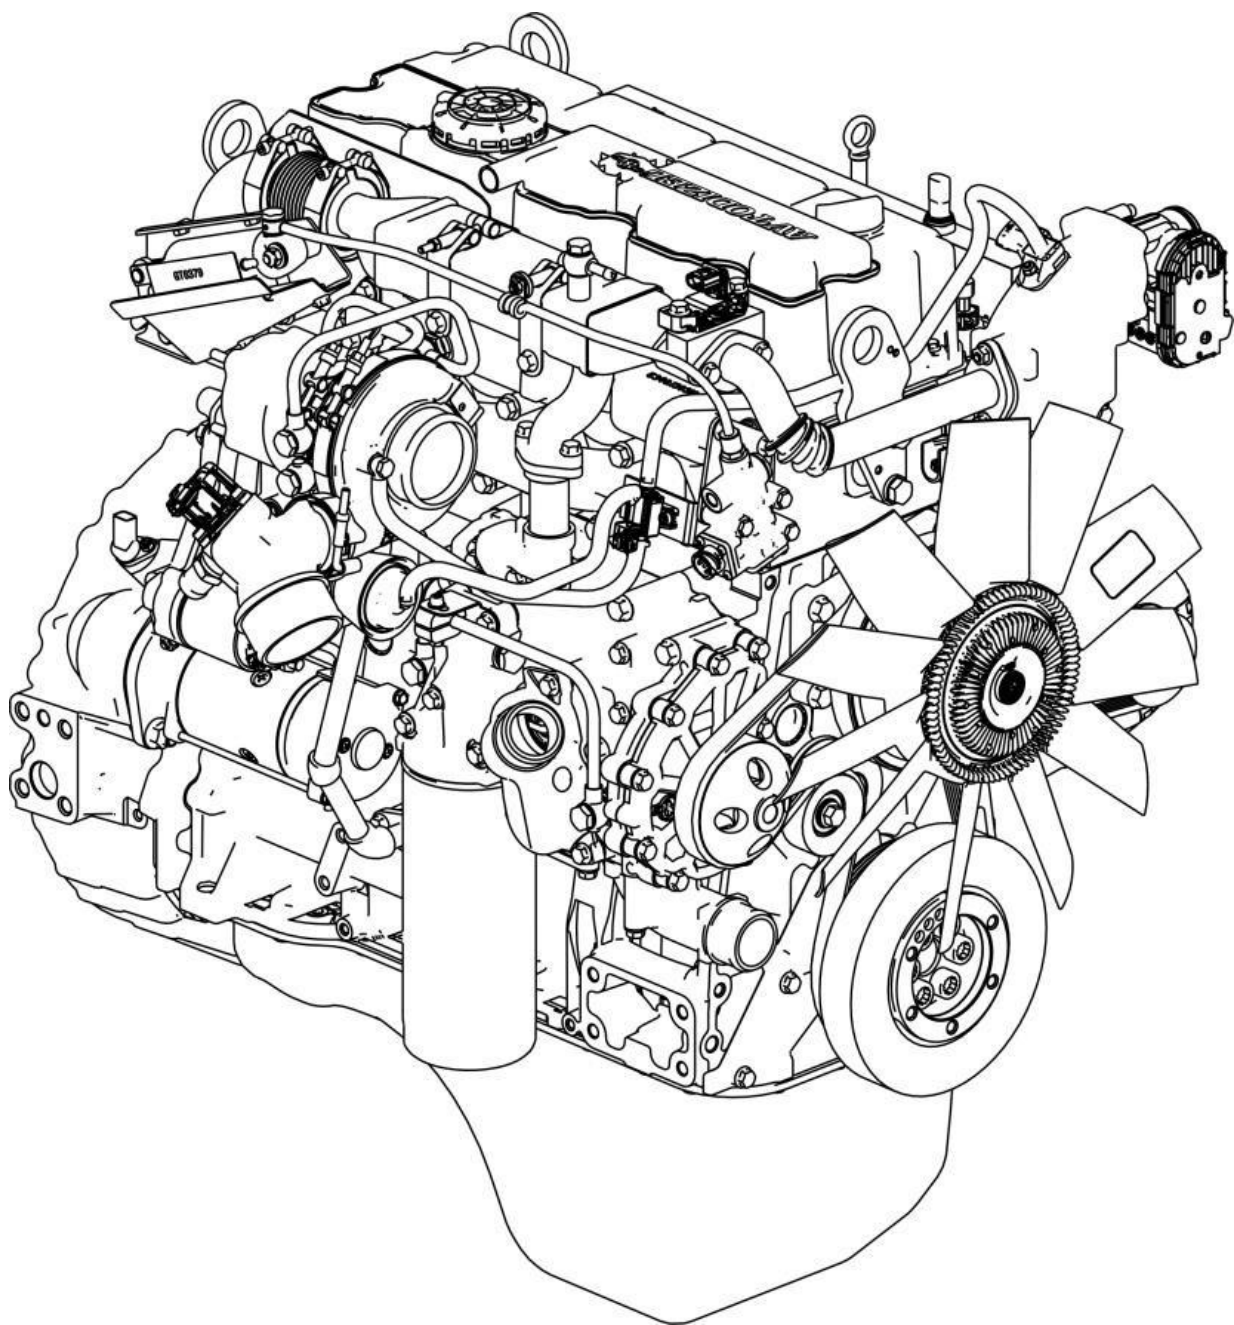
Двигатель ЯМЗ-53444-20 (общий вид справа)
